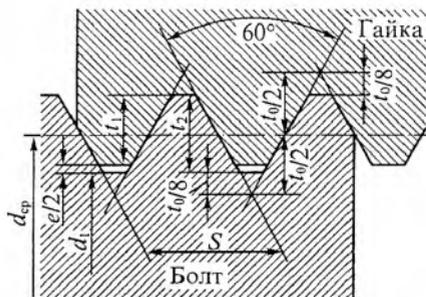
Метрическая резьба (размеры указаны в миллиметрах): $d_{\text{сп}}$ – средний диаметр резьбы; e – нормированный зазор; d_1 – внутренний диаметр резьбы; S – шаг резьбы; t_0 – теоретическая высота профиля; t_1 – расстояние между вершинами витков болта и гайки; t_2 – расстояние от вершины витка до дна впадины
